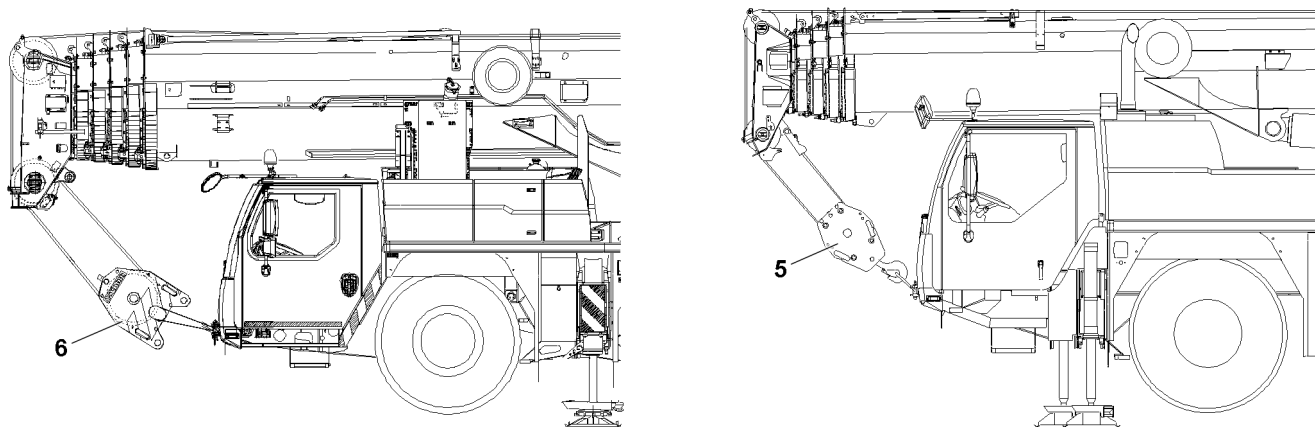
O conjunto de roldanas ou o moitão de gancho está engatado
